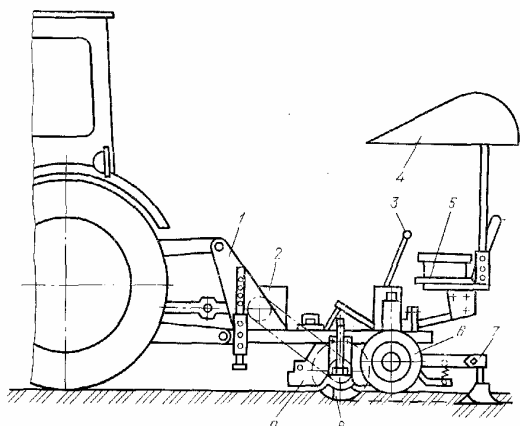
Культиватор фрезерный управляемый КФУ-1,5
